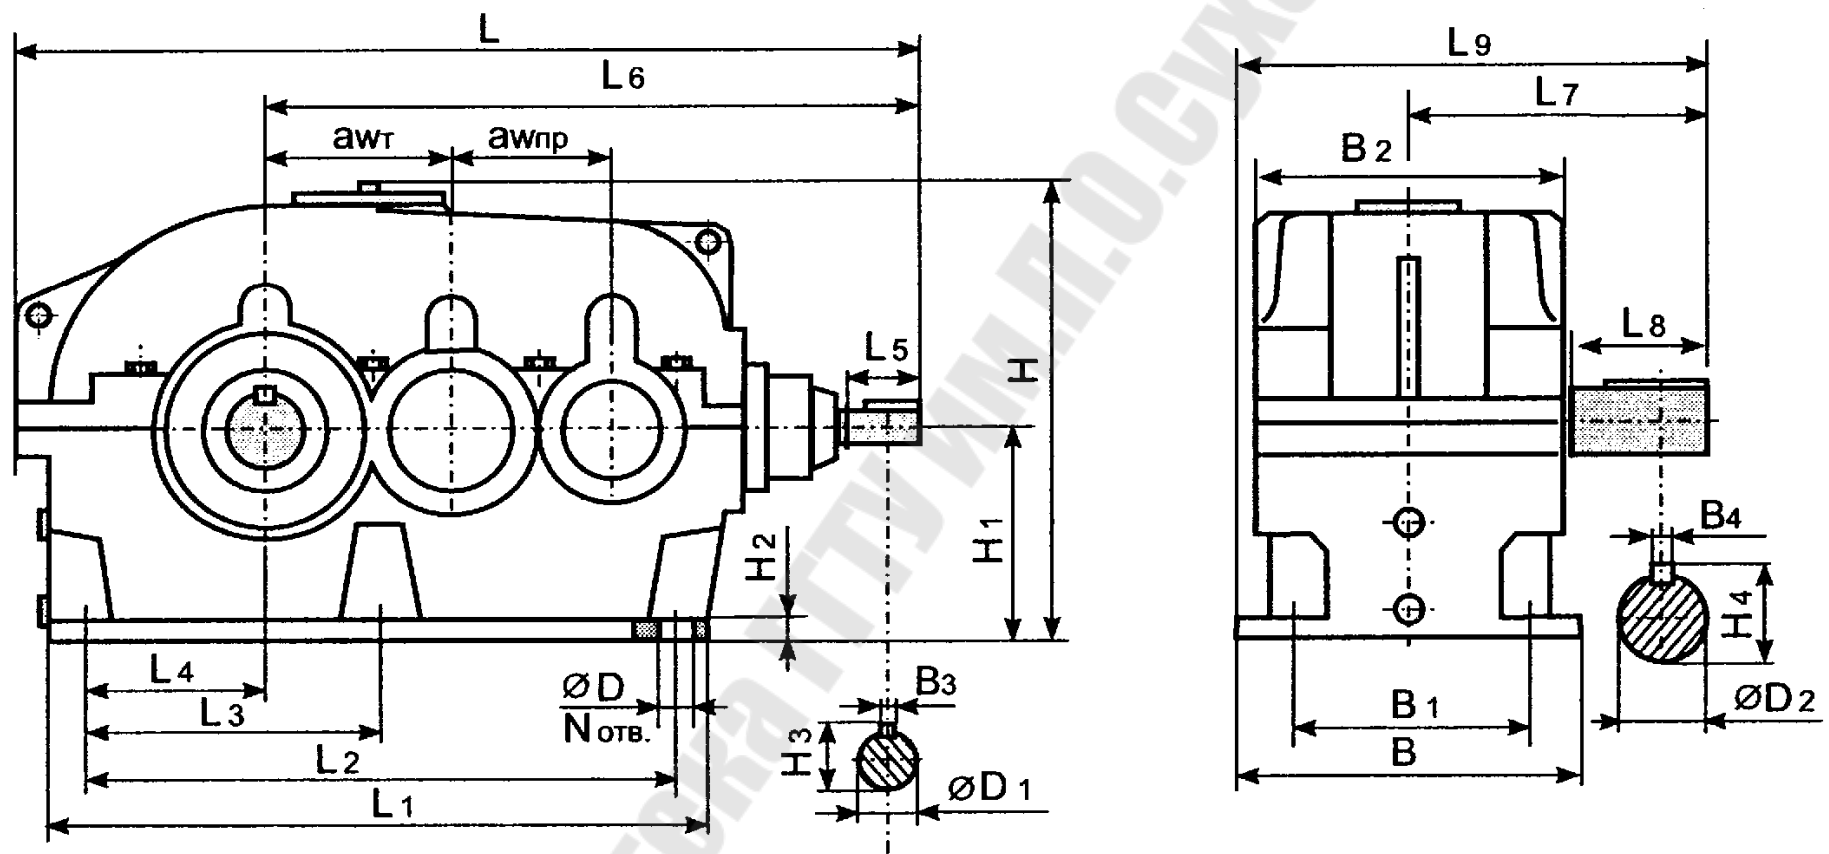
Редуктор коническо – цилиндрический трехступенчатый
